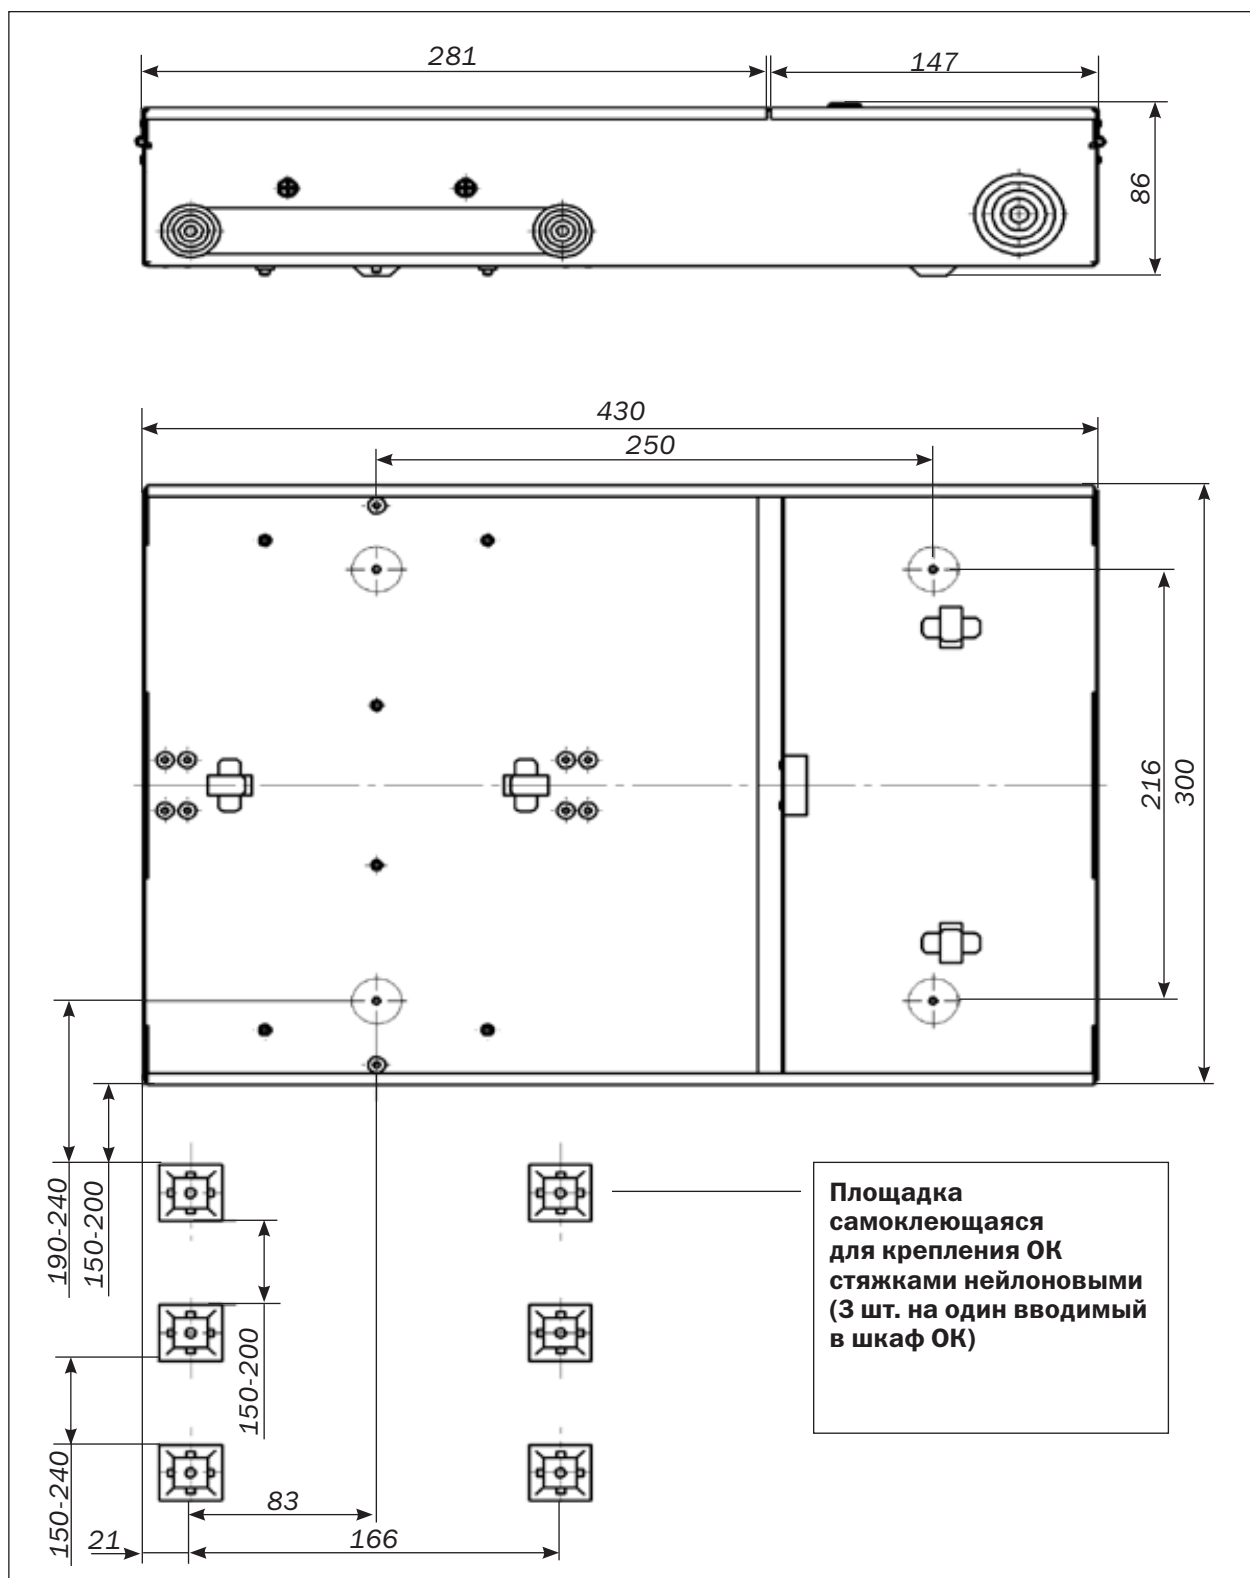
Габаритные и установочные размеры шкафа
